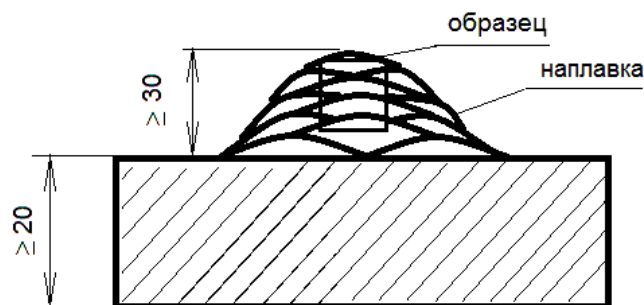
Схема изготовления образца для определения химического состава наплавленного металла
